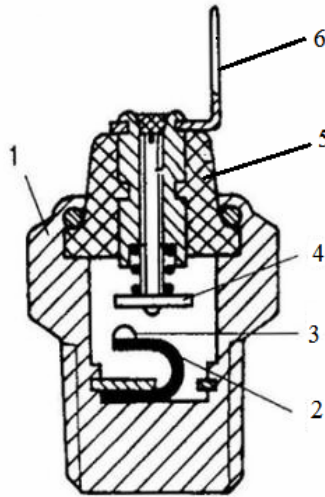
Термобиметаллический датчик: 1 – корпус; 2 – термобиметалл; 3 – подвижный контакт; 4 – неподвижный контакт; 5 – изолятор; 6 – электрический вывод
